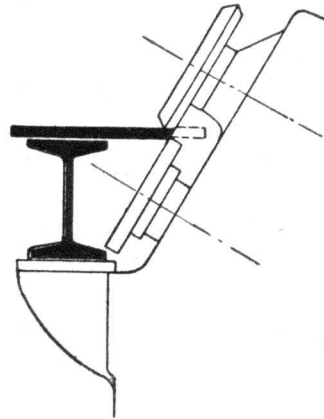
Stemmkantenschnitt an einer ebenen Platte.
